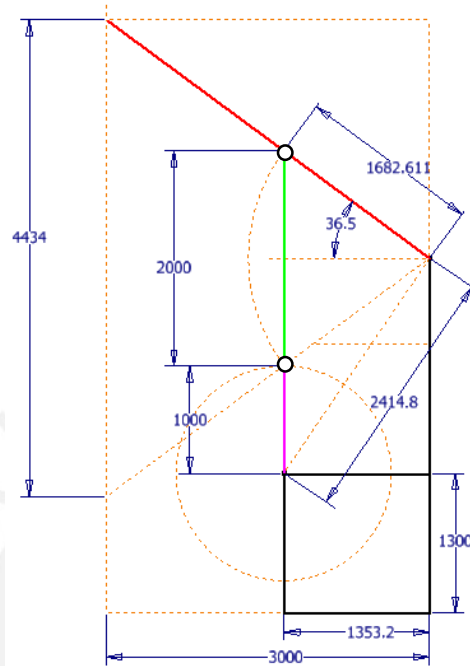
Propuesta dimensional del conector, manivela y balancín.
